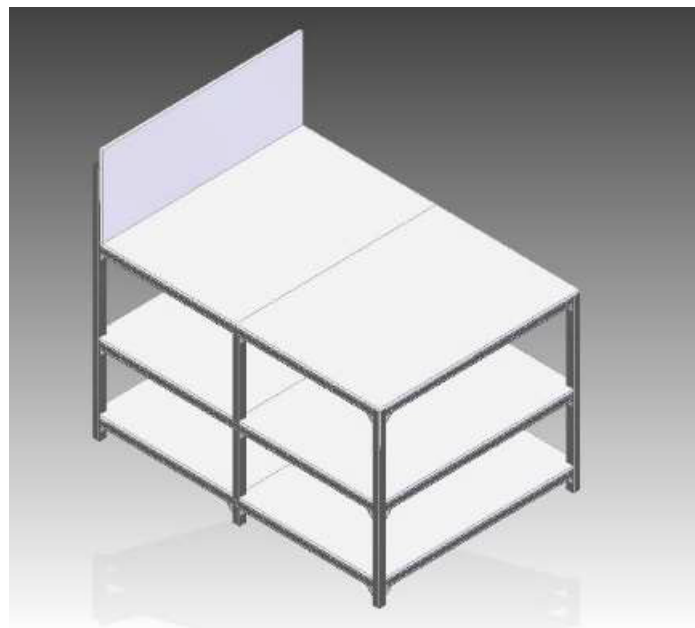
Modelado 3D de la sección estructural. Fuente: [2]
